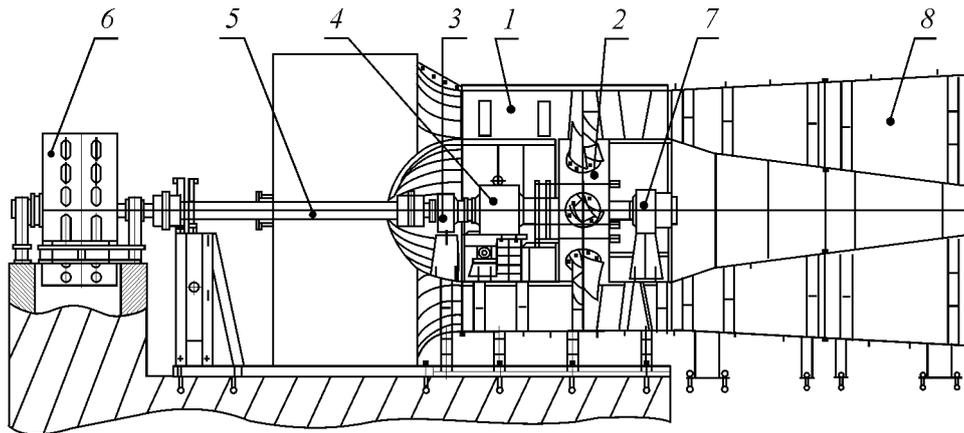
Компонновка вентиляторных агрегатов ряда осевых вентиляторов серии ВО: 1 — вентилятор; 2 — рабочее колесо со съемными листовыми лопатками; 3 — радиальная подшипниковая опора; 4 — механизм поворота лопаток РК; 5 — трансмиссионный вал; 6 — синхронный (асинхронный) электродвигатель; 7 — радиально-упорная подшипниковая опора; 8 — диффузор
